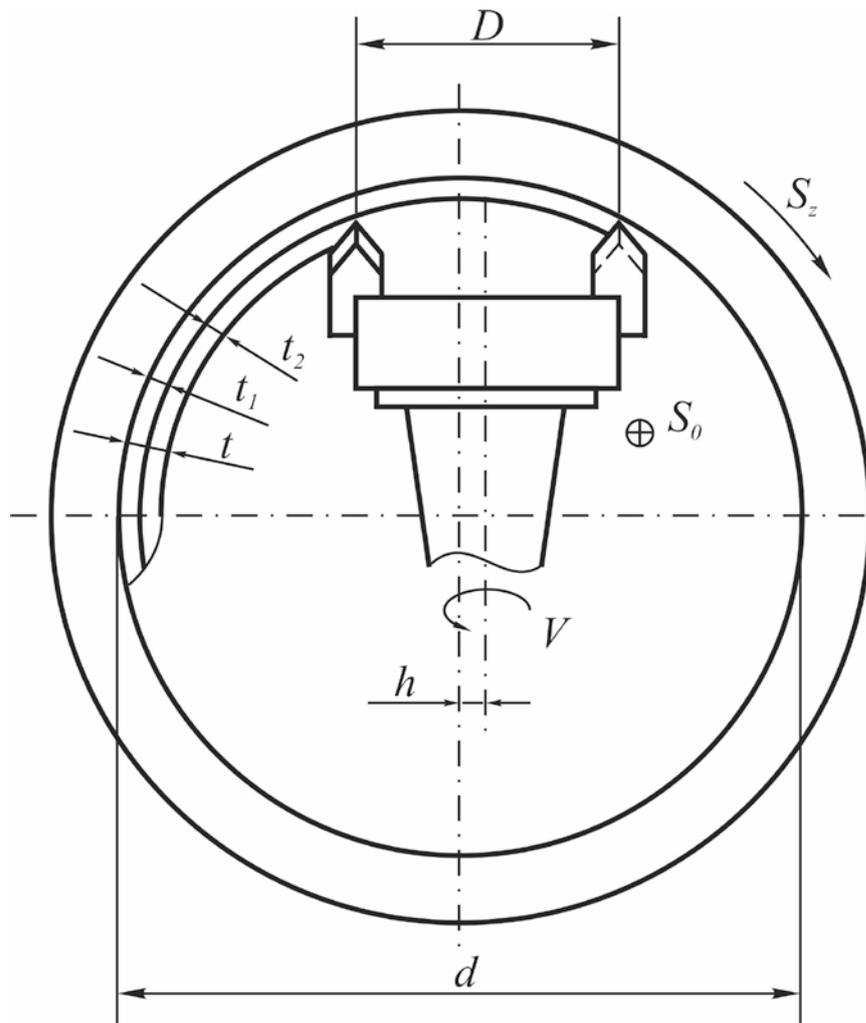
Кинематическая схема обработки внутренних поверхностей вращения фрезами с двумя режущими кромками
